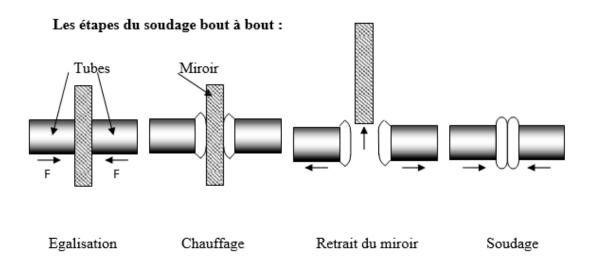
Les étapes du soudage bout à bout [60]
